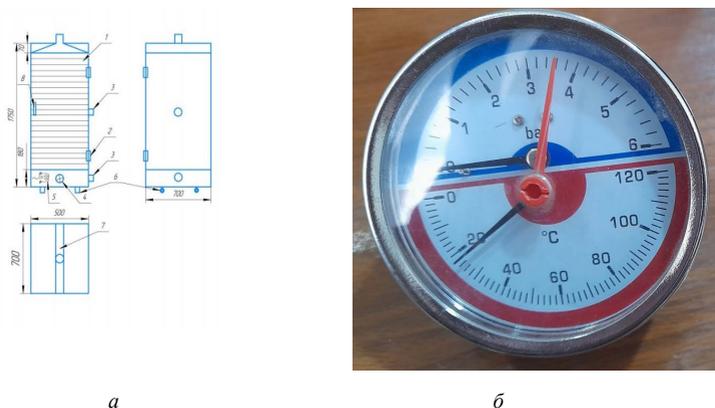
Кинематическая схема и габаритные размеры сушильного шкафа (а) и (б) вид термометра-барометра: 1 – стеклянная дверь сушильного шкафа; 2 – петля двери шкафа; 3 – термометр-барометр; 4 – вентилятор; 5 – нагревательный элемент; 6 – колесо для передвижения шкафа
